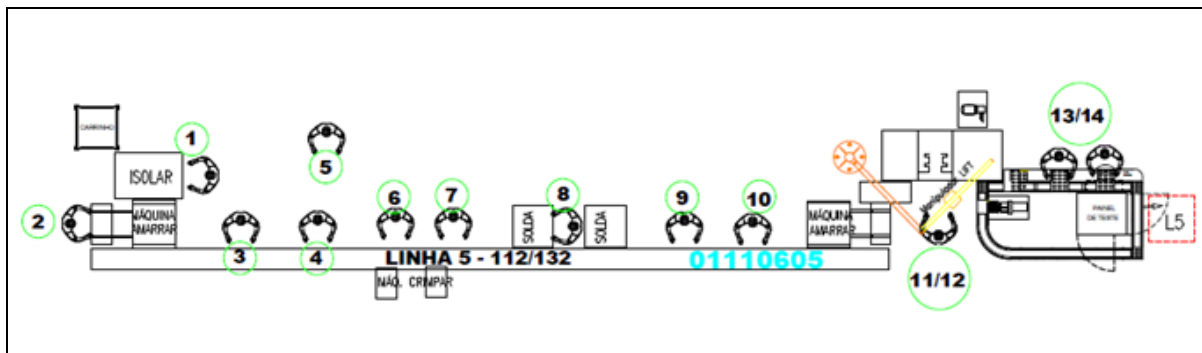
está apresentado o layout proposto, conforme as adequações propostas.
